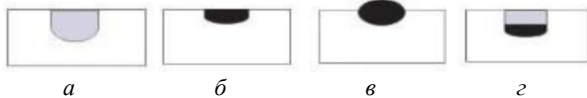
Типи впливу лазерного випромінювання на поверхню оброблюваного матеріалу:
